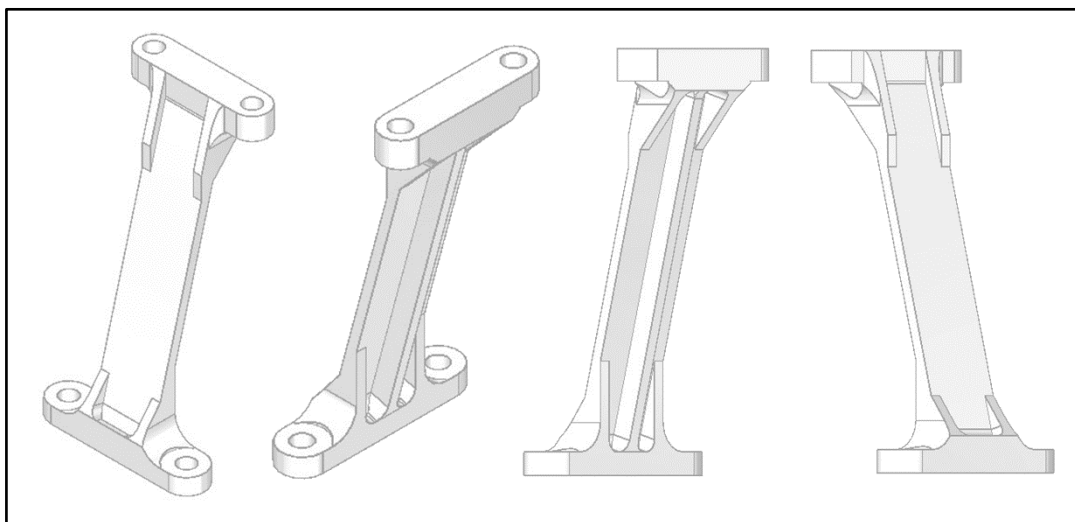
Vistas dos suportes estruturais reforçados.
